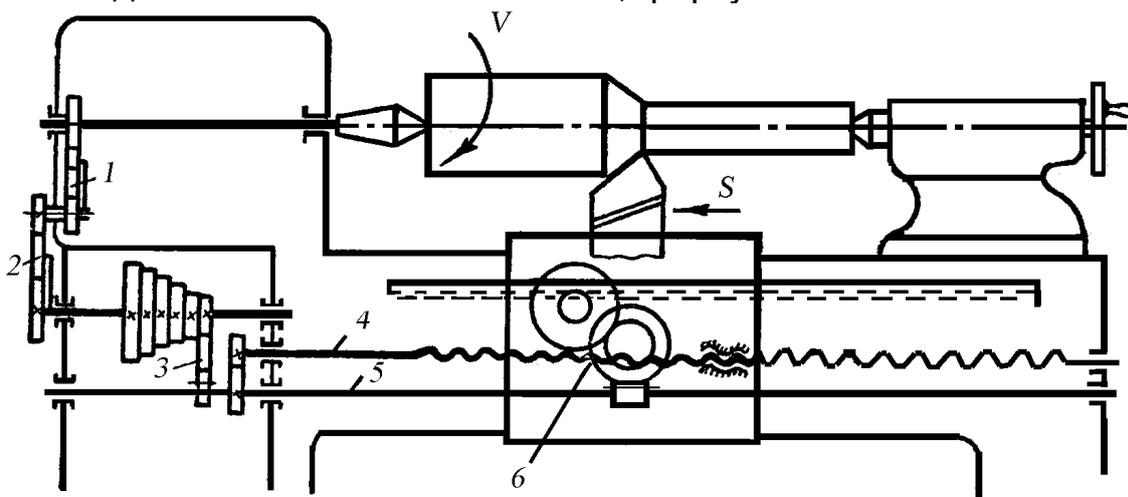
Схема привода движения подачи токарного станка: 1 – реверсивный механизм; 2 – гитара; 3 – коробка передач; 4 – ходовой винт; 5 – валик; 6 – фартук
